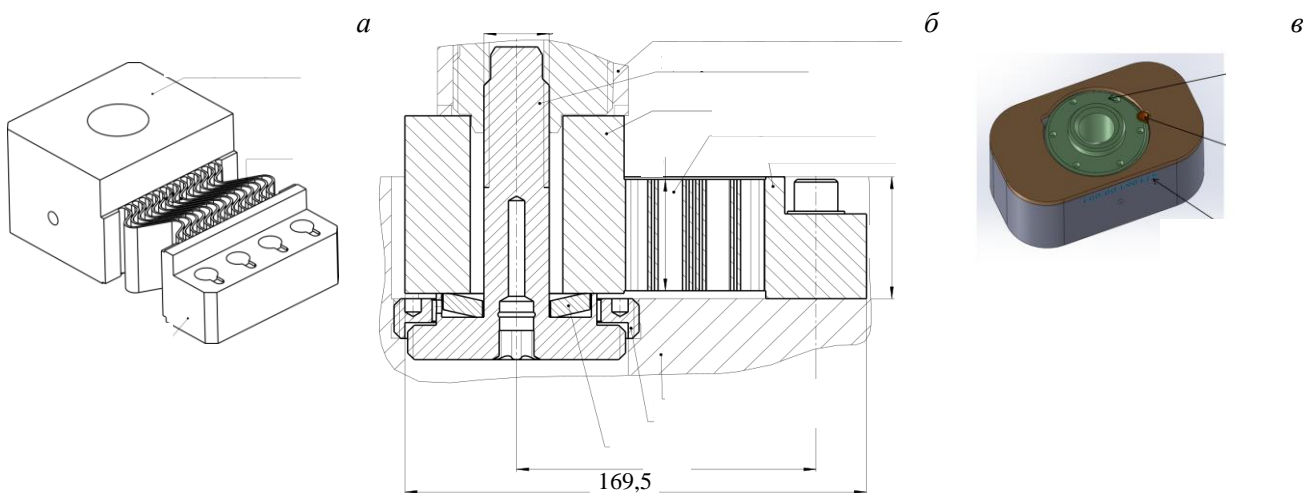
Общий вид ЭС МБ/ВК (а); общий вид пьедестала ЭС (б); ЭС с элементами крепления (в)
